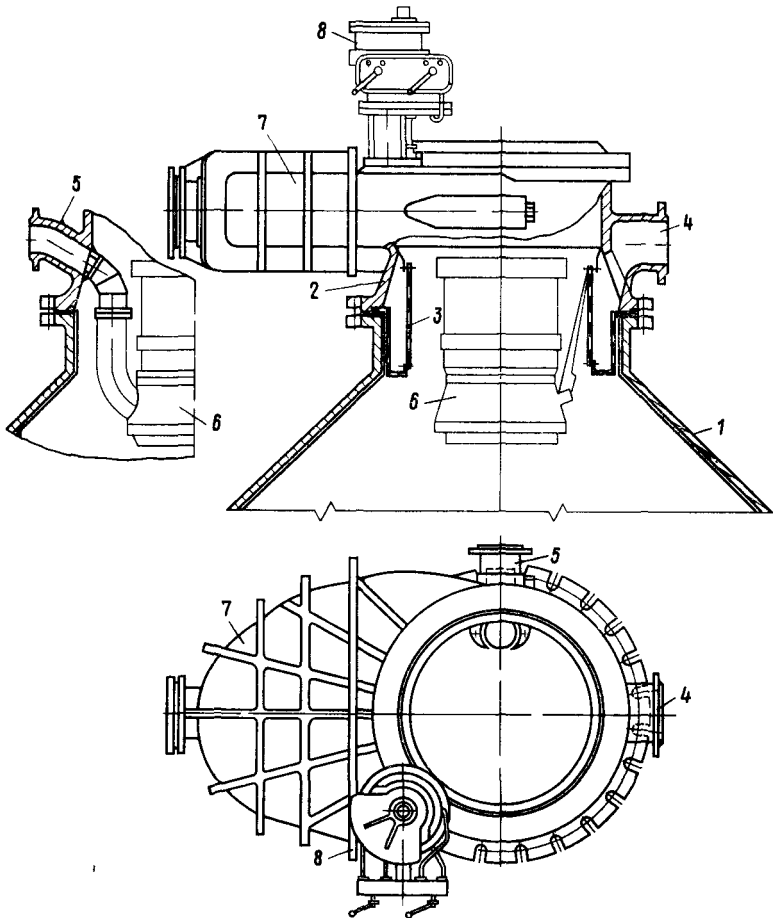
Верхняя горловина биметаллического сварного котла с автоматической крышкой
